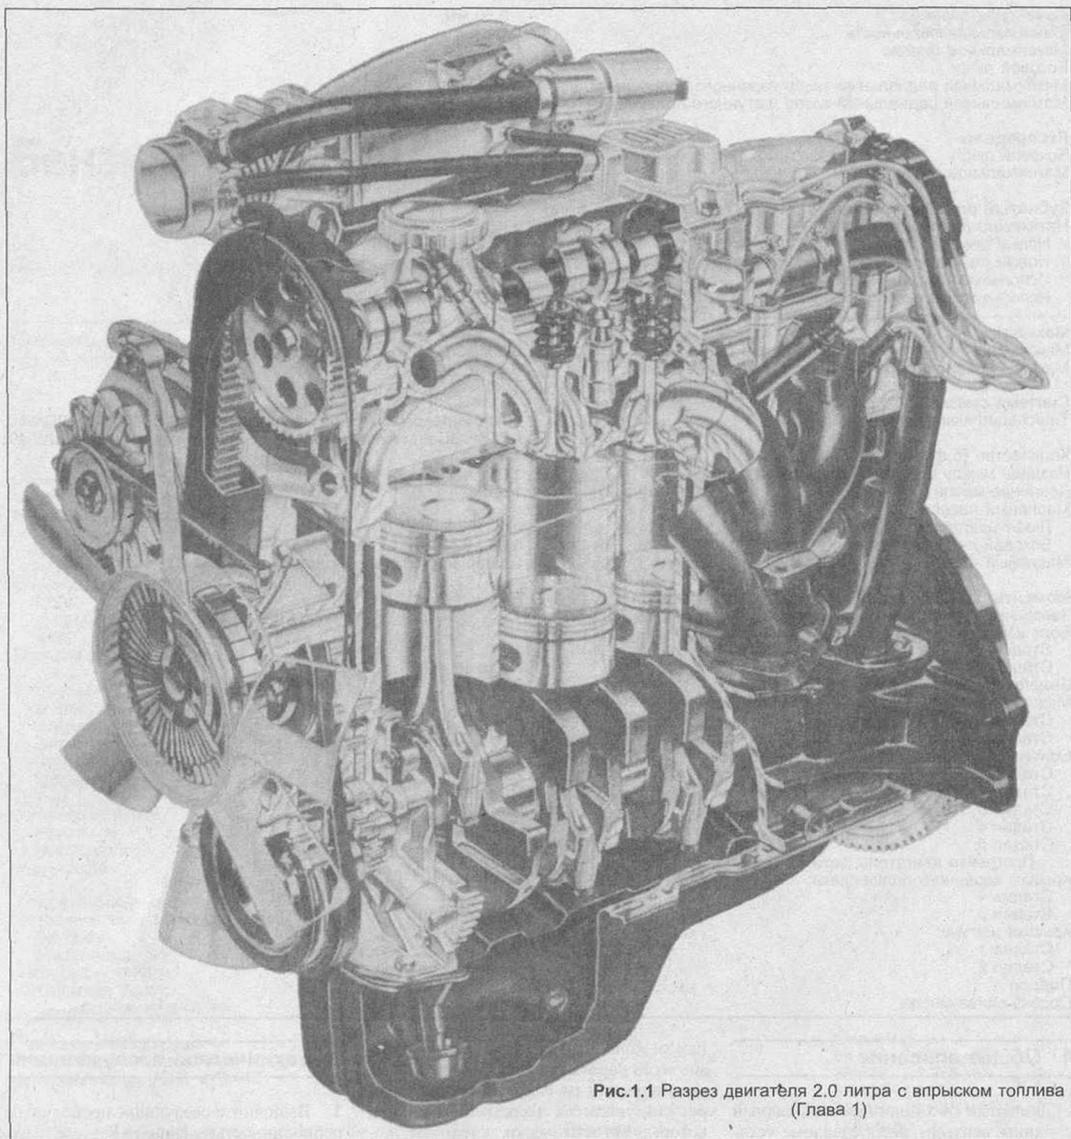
Разрез двигателя 2.0 литра с впрыском топлива
